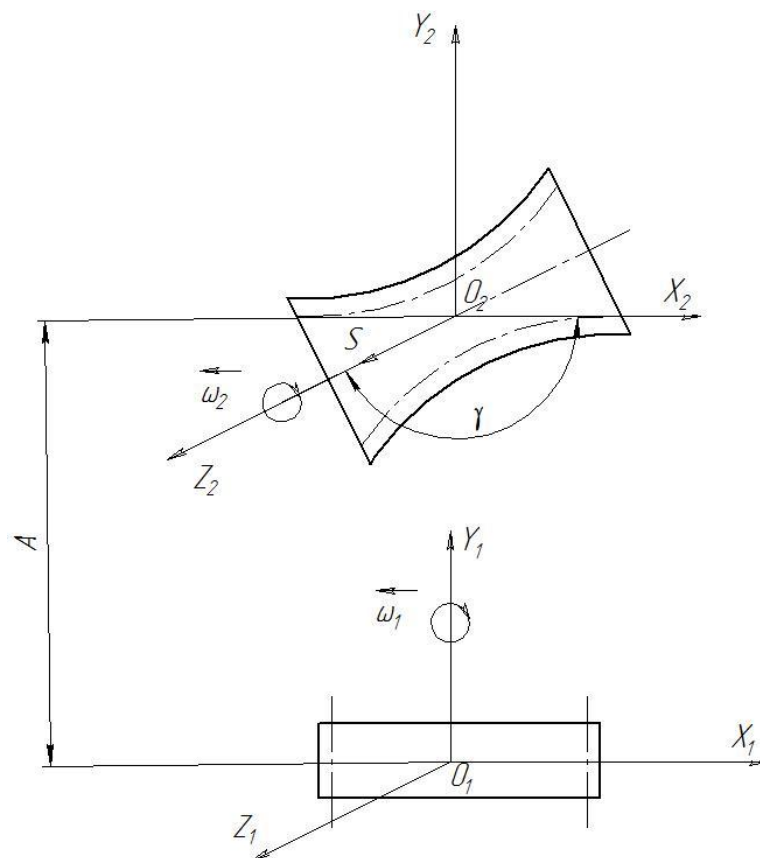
Схема притирки зубьев цилиндрического зубчатого колеса винтовым гиперболоидным притиром
